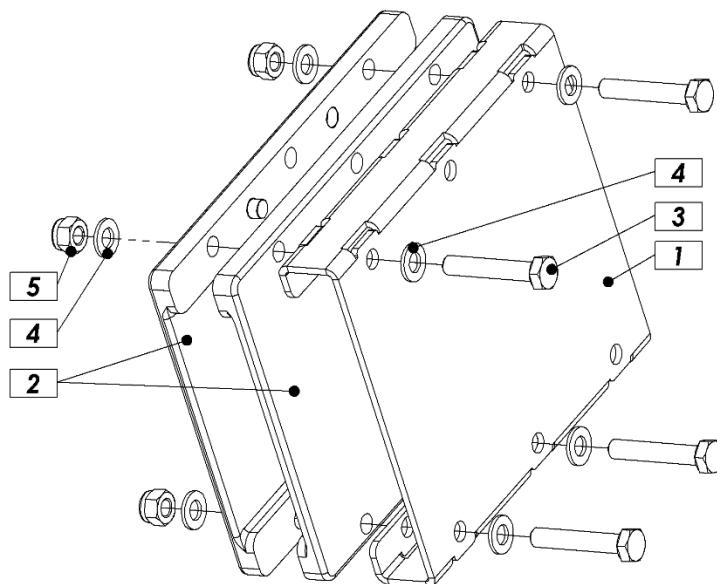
5006.13.20.0 – Motorsäge-Träger
